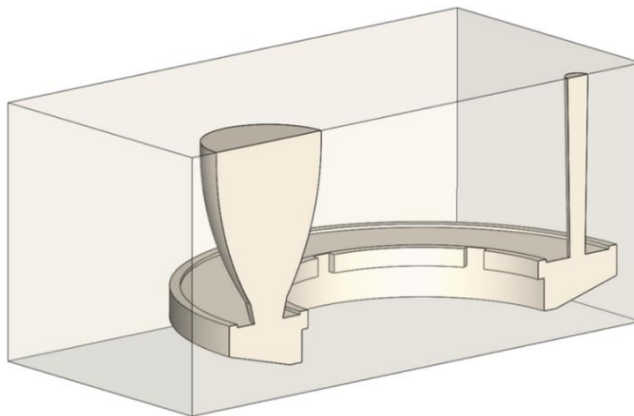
Разрез отливки «Кольцо» с литниковой системой
